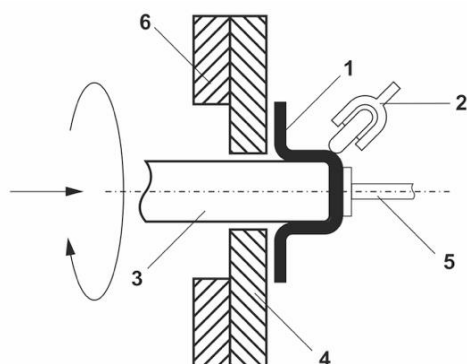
Схема формообразования полый листовой детали методом обкатки с автоматической подачей оправки на станке с ЧПУ:
